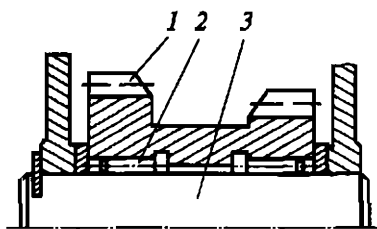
Блок зубчатых колес на игольчатых роликах без колец:
